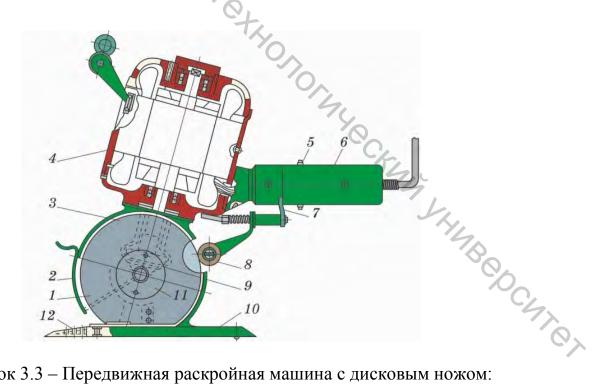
Передвижная раскройная машина с дисковым ножом: 1 – дисковый нож, 2 – щиток, 3 – стойка, 4 – электродвигатель, 5 – выключатель, 6 – рукоятка, 7 – пусковая кнопка, 8 – устройство заточки ножа, 9 – коническая шестерня, 10 – платформа, 11 – коническая шестерня, 12 – козырек
